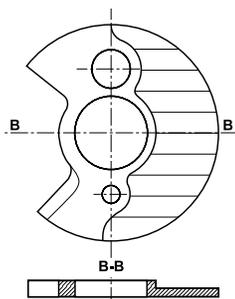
Верхний золотник двухкарбюраторного "Вихря-30".
